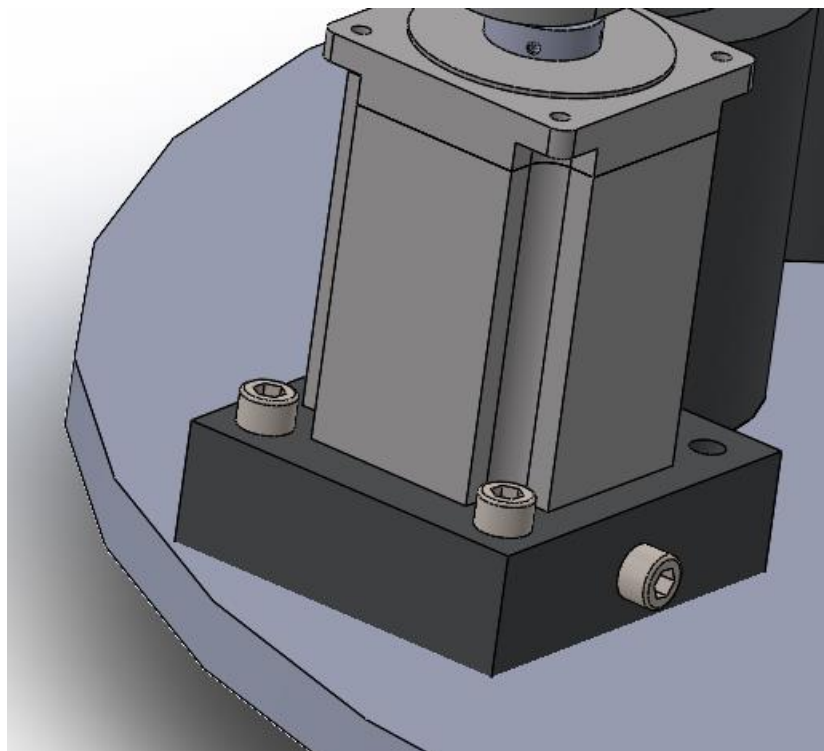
Крепление двигателя к нижней платформе
